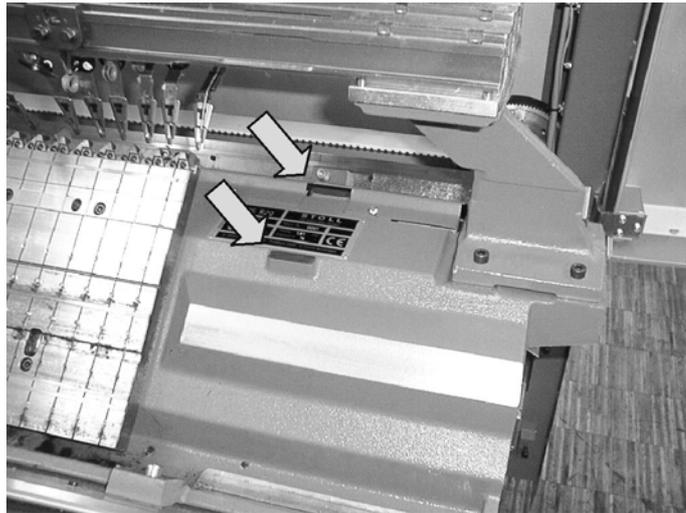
Rechte Auflagefläche für die Wasserwaage
